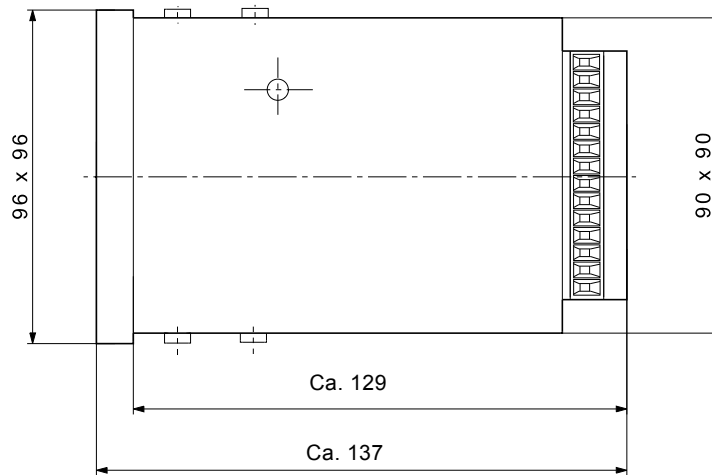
Maßzeichnung / Bohrbild für Conex® DIA-1 / Conex® DIA-2Q zur Wandmontage der Steuerung
